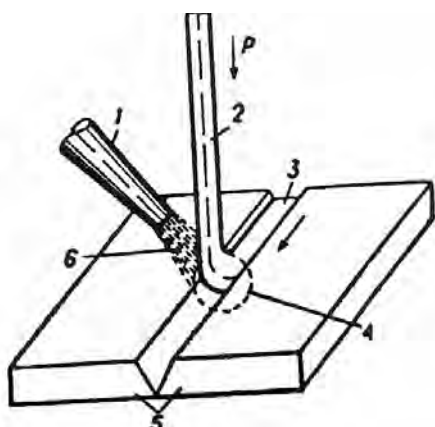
Схема сварки пластмасс с применением присадочного материала:
